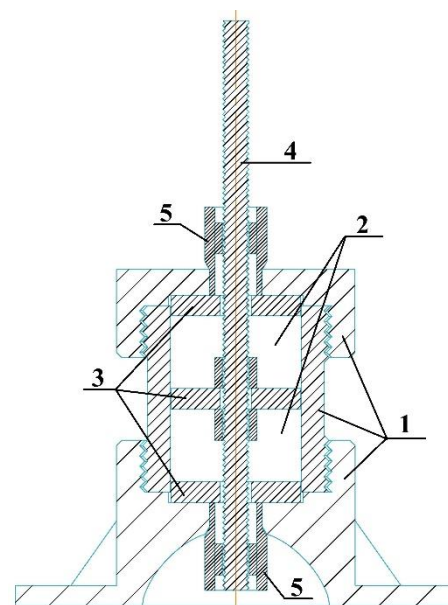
Конструкция демпфера: 1 – пластиковый корпус, 2 – опытный образец (эластомер), 3 – неодимовые магниты, 4 – направляющий стержень, 5 - гайки
